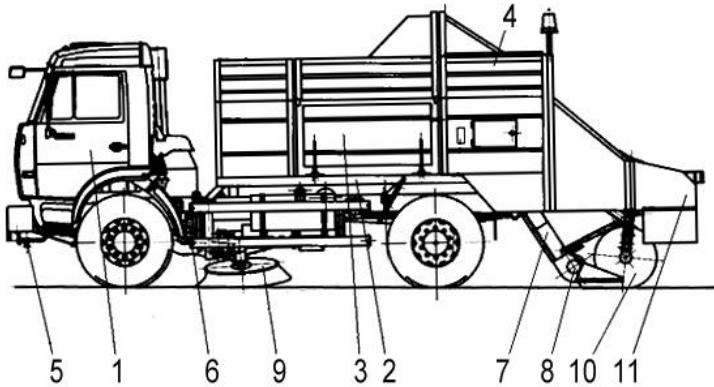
Конструктивная схема самоходной подметально-уборочной машины с механической загрузкой бункера:
